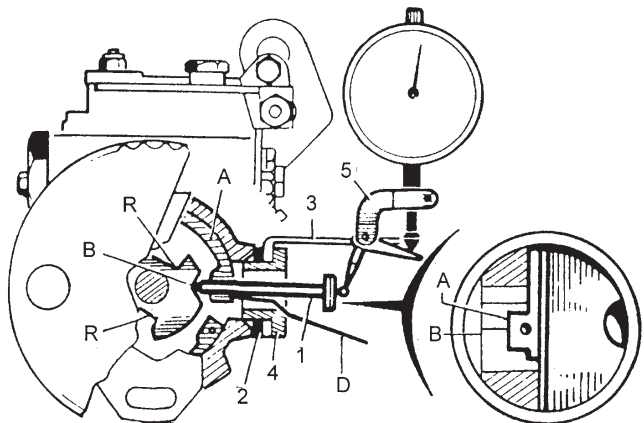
Установка приспособления с индикатором через смотровое окно: А - кольцо, В - фазовая канавка, D - зажим, R - фрезерованное углубление; 1 - регулировочный штифт, 2 - шайба, 3 - держатель индикатора, 4 - гайка, 5 - угольник поворотной планки.
